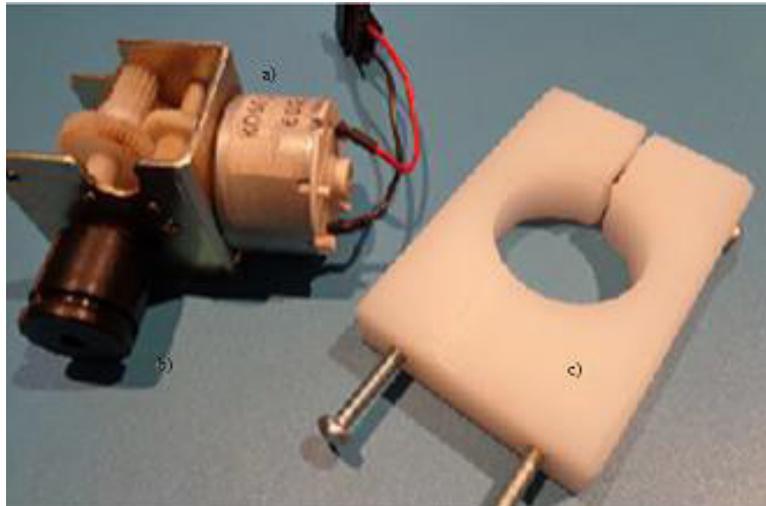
Mini motorreductor; a) Mini-motorreductor reversible, b) Polea incorporada, c) Acople elaborado a la medida del motor, tornillos de sujeción insertados.
